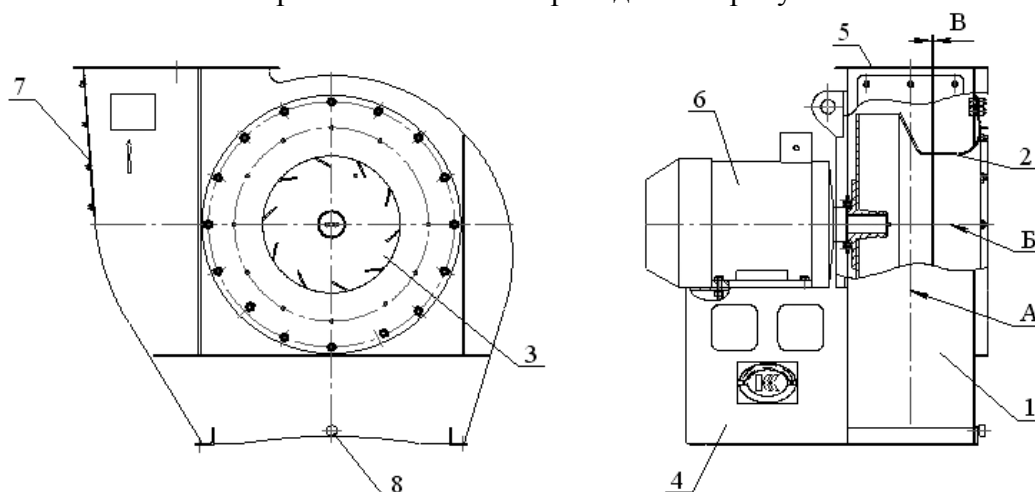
Вентиляторы ВПИ-PRU-630. Конструкция и состав.
